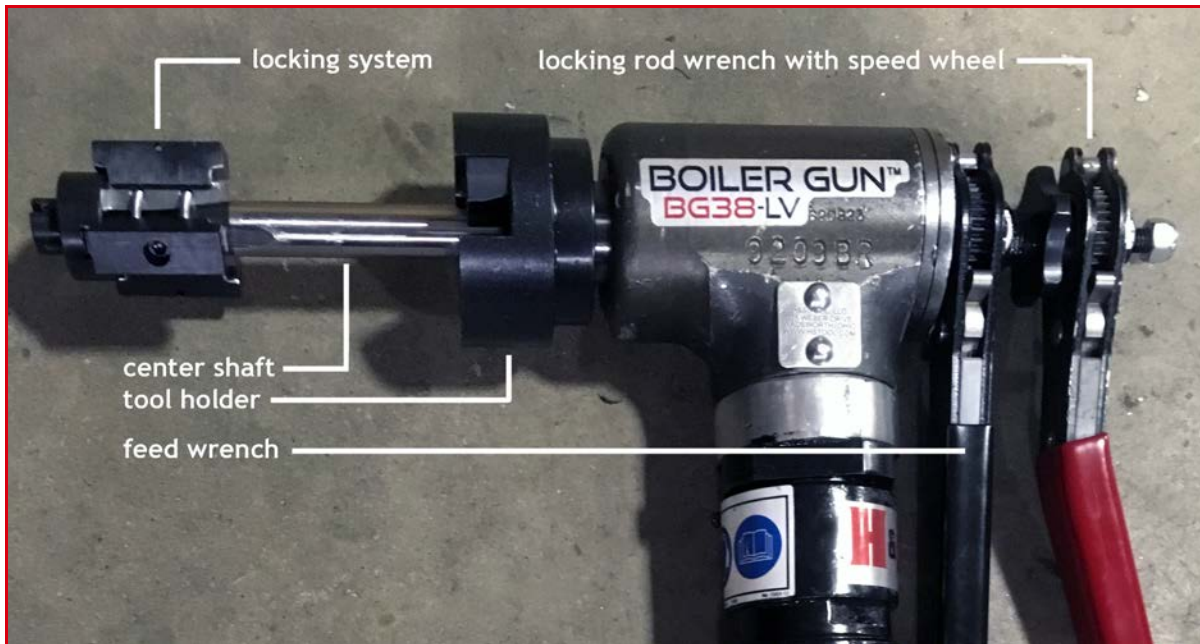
PRINCIPAUX COMPOSANTS DE LA BG38 BOILER GUN
